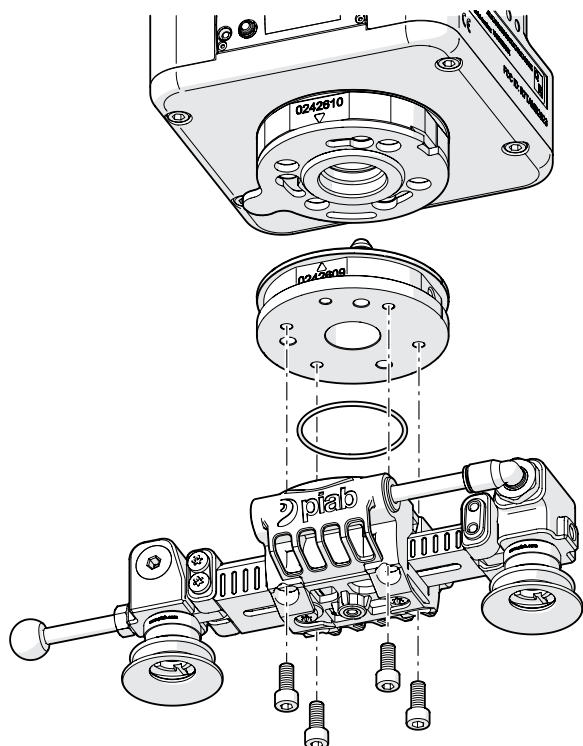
Przyssawka zamontowana na piCOBOT® Electric.
